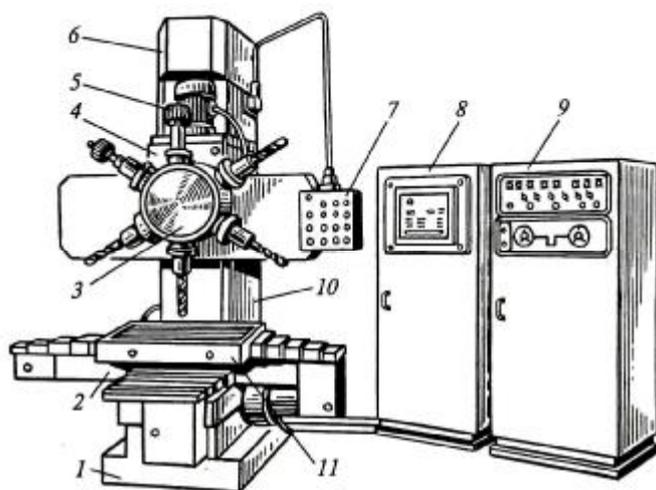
Станок вертикально-сверлильный с ЧПУ: 1 – основание; 2 – стол крестовый; 3 – головка револьверная; 4 – стойка; 5 – инструмент; 6 – электродвигатель поворота револьверной головки; 7 – пульт управления; 8 – шкаф электрооборудования; 9 – шкаф с ЧПУ
